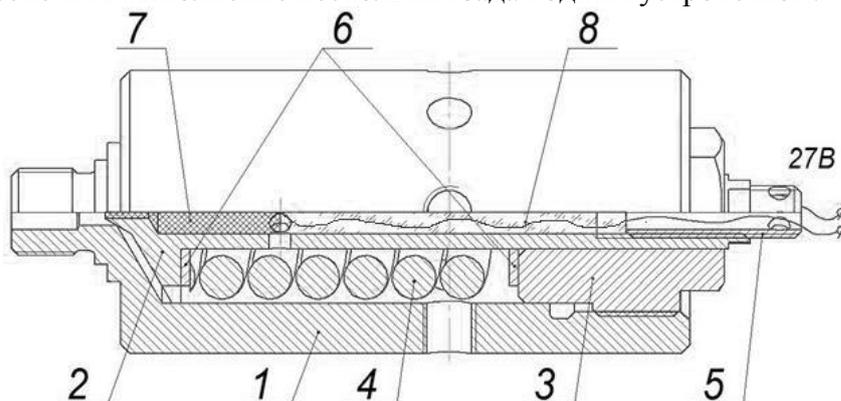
Двухконтурный предохранительный клапан. 1 – силовой корпус, 2 – седло, 3 – прижимная гайка, 4 – пружина, 5 – прижимная шпилька, 6 – прокладка, 7 – заряд ЭКС, 8 – стеклянная втулка
